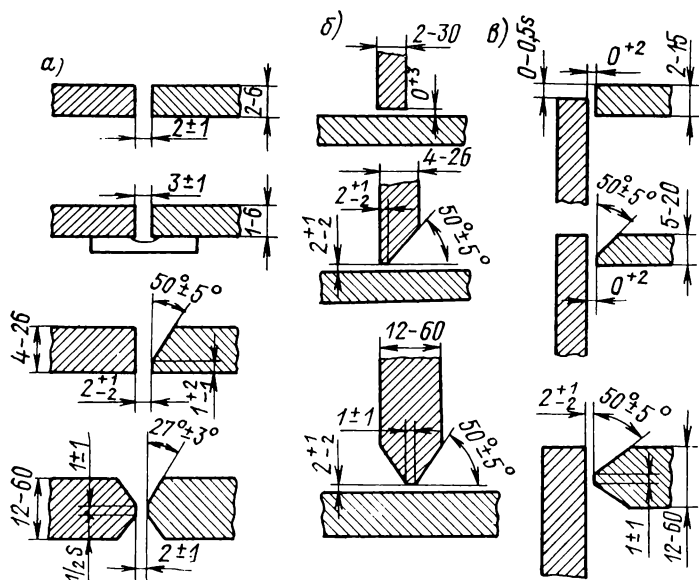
Конструктивные элементы подготовки кромок (а) стыковых, (б) тавровых и (в) угловых соединений под автоматическую сварку в двуокиси углерода.
